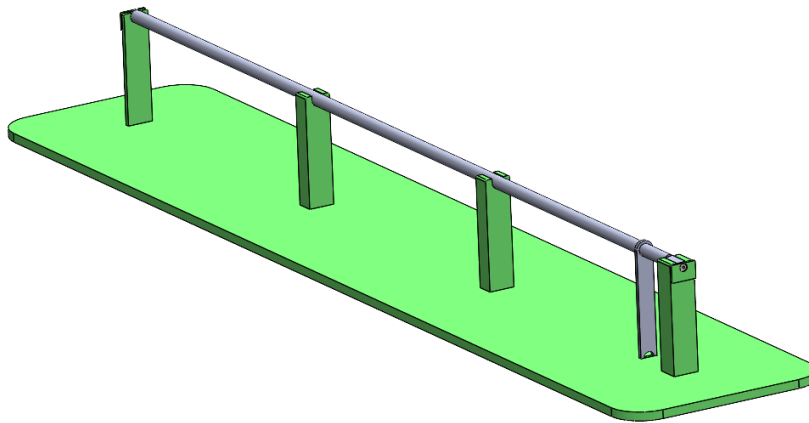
Ferramenta de soldadura do braço ao veio motriz
